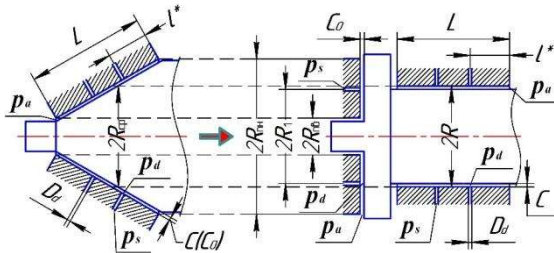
Розрахункова схема багатоопорного безконтактного приводу
